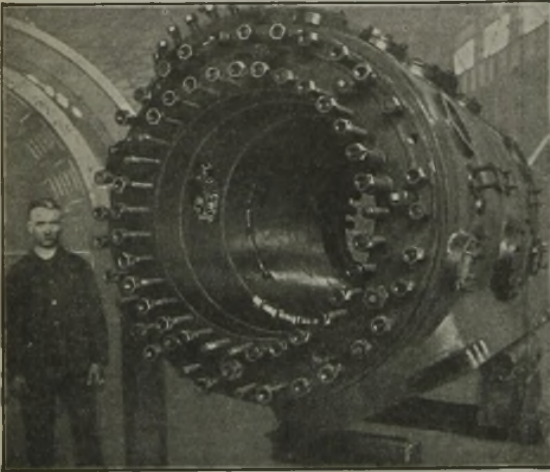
Geschweißter Großgasmaschinen-Zylinder.
